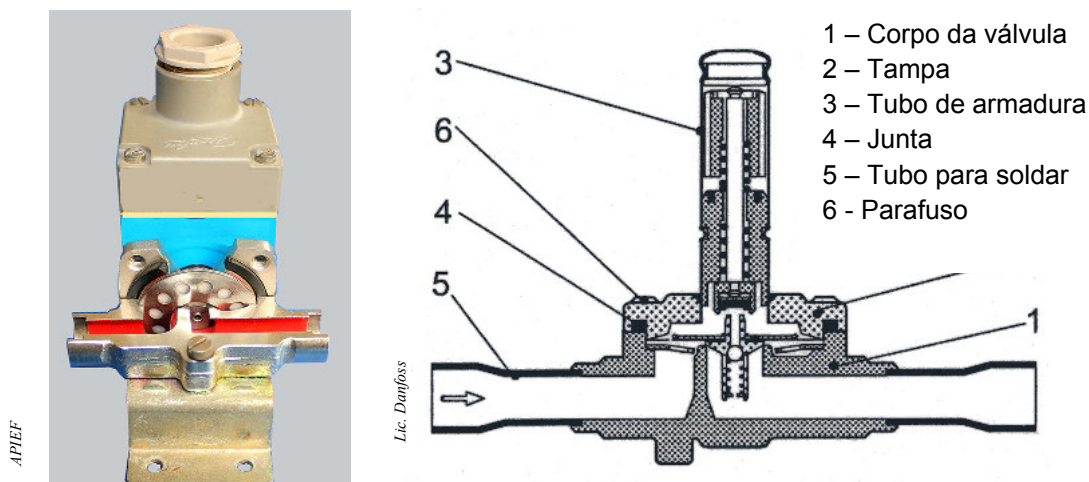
Válvula de solenóide (representada em esquema sem bobina)
